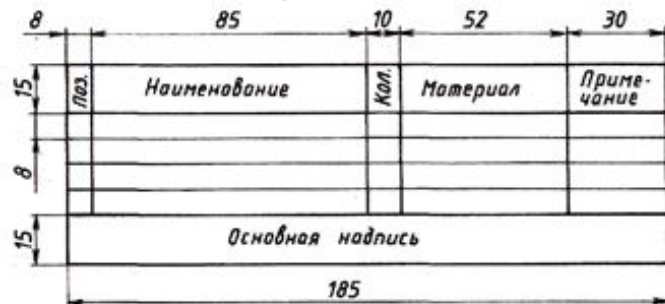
Форма и размеры спецификации для учебного сборочного чертежа
